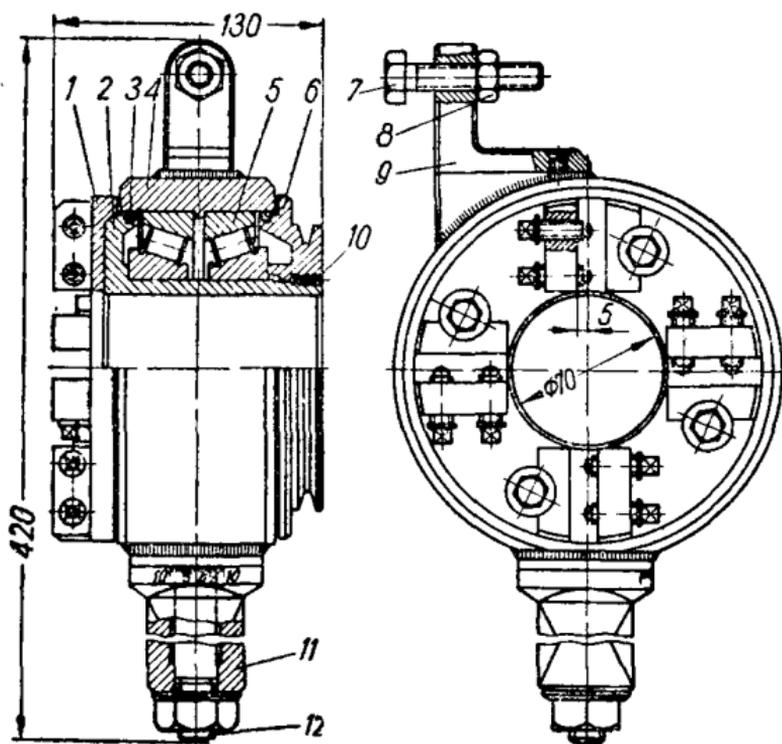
Приспособление для вихревого нарезания наружной резьбы.
